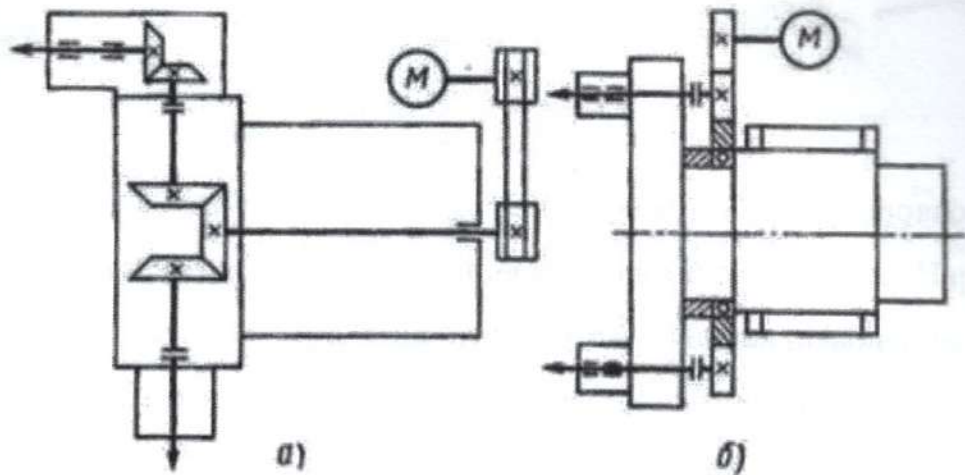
Револьверні головки токарних верстатів з обертовим інструментом
